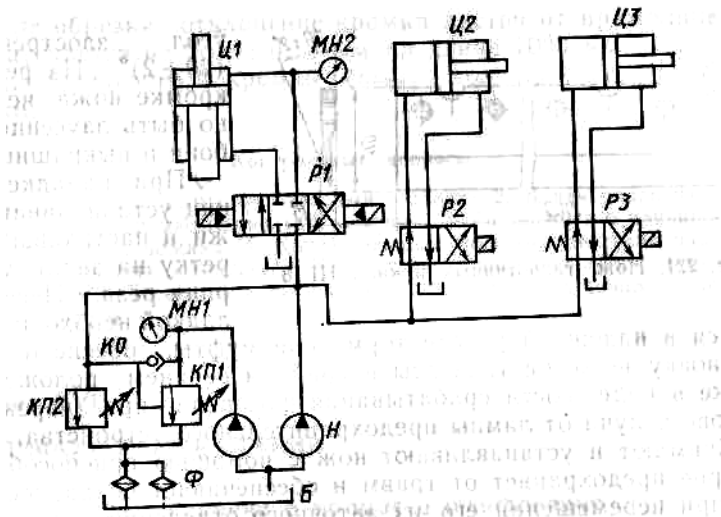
Гидравлическая схема гильотинных ножниц НГ18: Н — насосы, КП1, КП2 — предохранительные клапаны, КО — обратный клапан, P1 — основной распределитель, Ц1 — гидроцилиндр подъема траверсы, Ц2, Ц3 — гидроцилиндры привода упоров, P2, P3 — распределители управления упорами, Ф — фильтр, Б — бак
